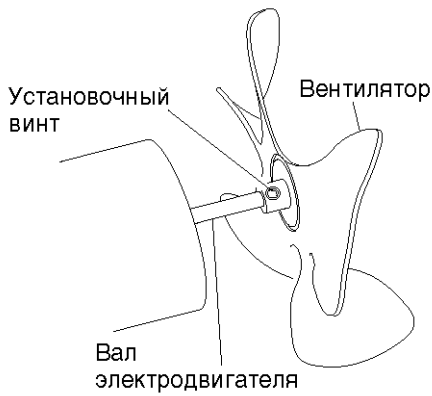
, Расположение вентилятора, вала электродвигателя и установочного винта
